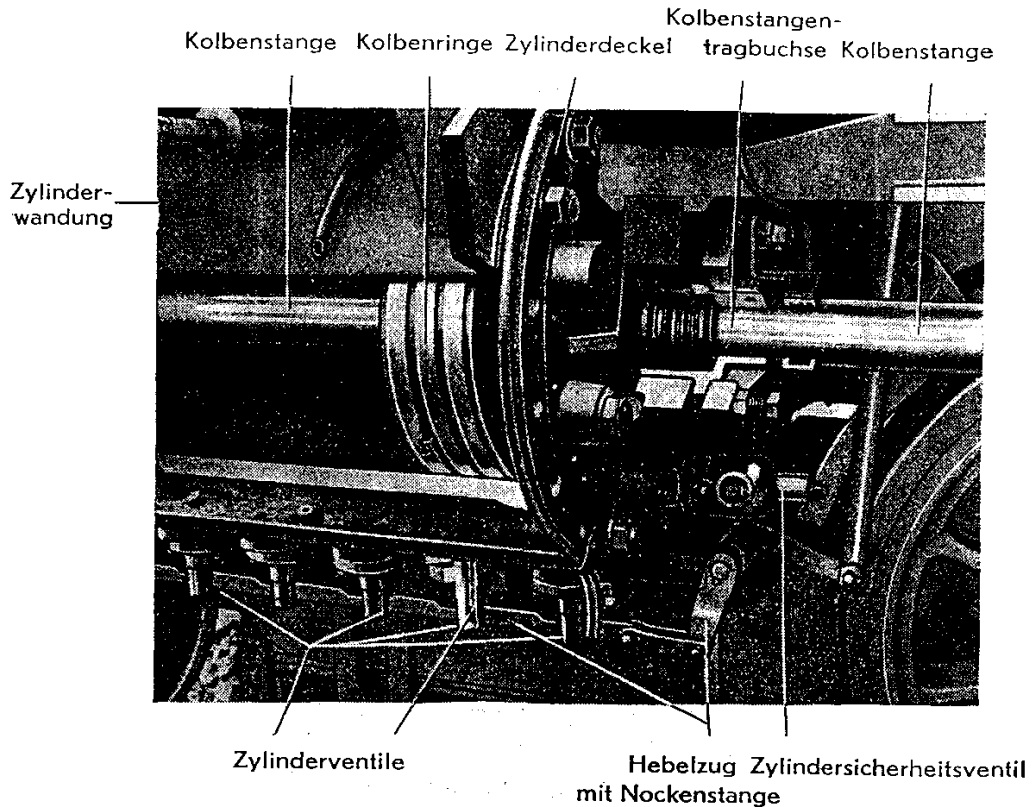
Aufgeschnittener Dampfzylinder, ein Zylinderventil, ein Zylinderblock, eine Kolbenstangentragbuchse geschnitten
